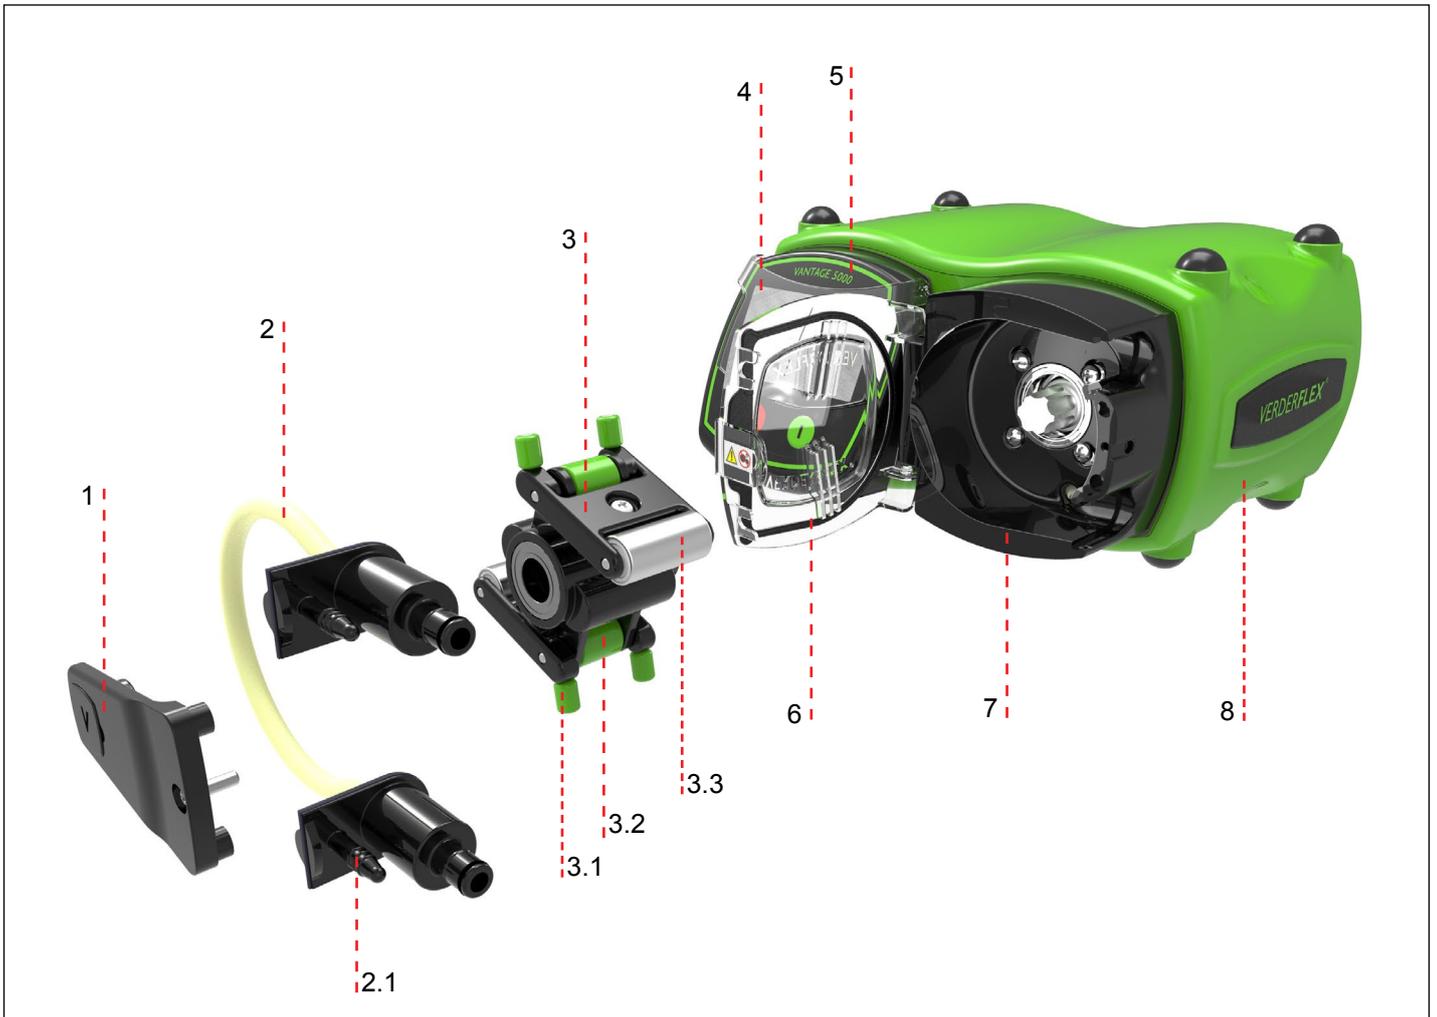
Vue éclatée de la Vantage 5000 – Élément tubulaire
